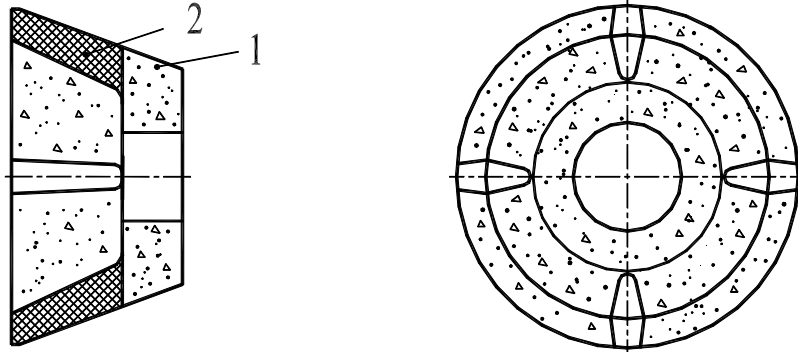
КШК чашечный конический (тип 11): 1 – ПШК; 2 – твердый смазочный материал.
